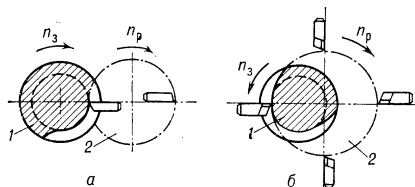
Схема вихревого нарезания резьбы: а — методом охватывания; б — методом огибания; 1 — заготовка; 2 — резцовая головка; n_3 — направление вращения заготовки; n_p — направление вращения резцовой головки.
